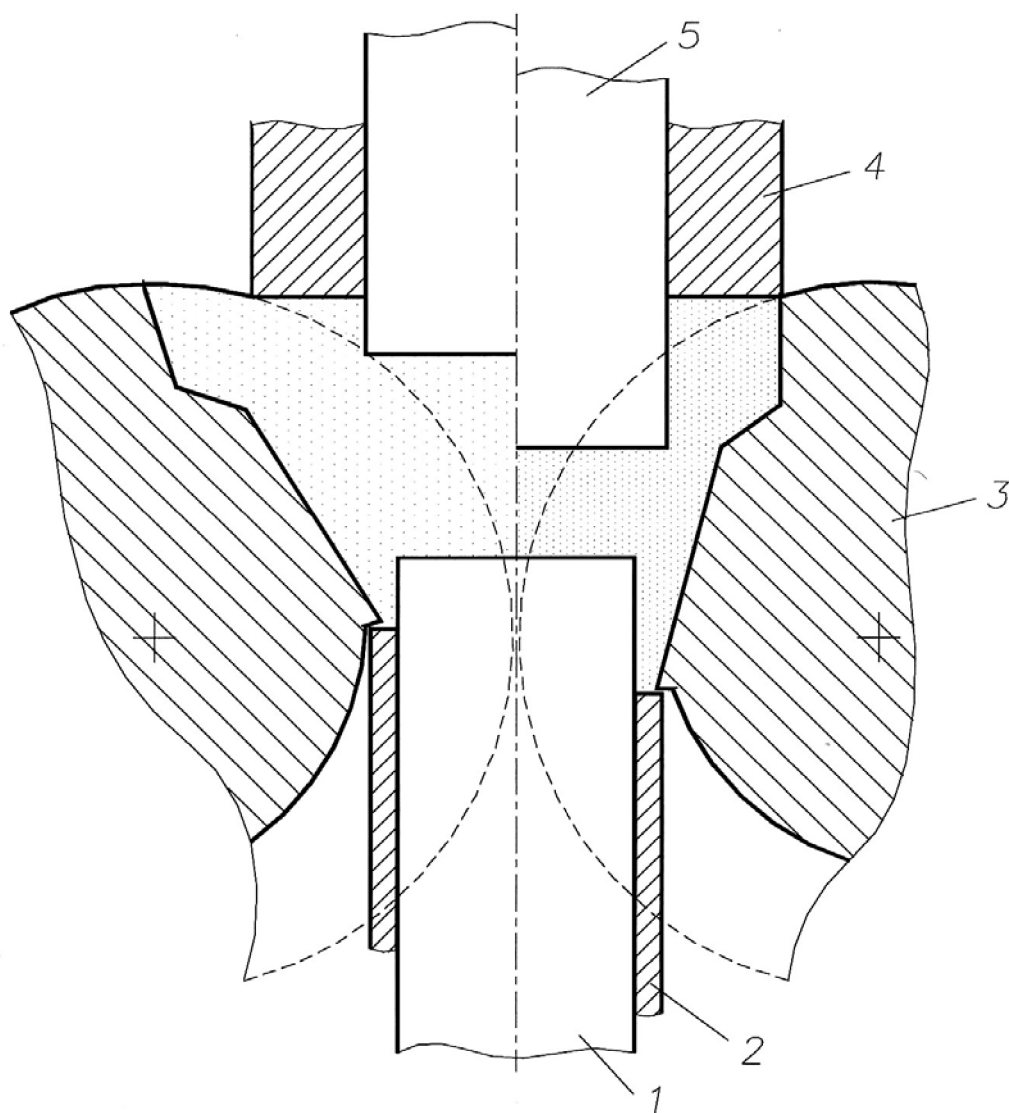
Формование порошковой заготовки в матрице, образованной вальцами
